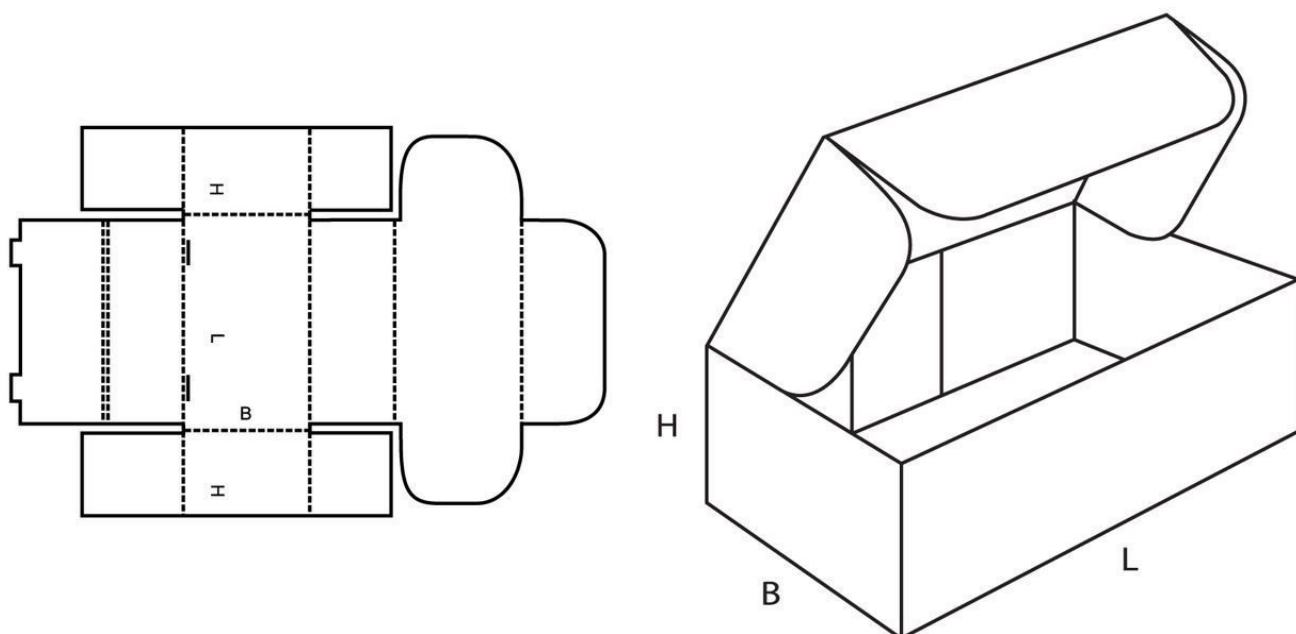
Чертеж выкройки и общего вида картонной коробки безклеевой сборки:
